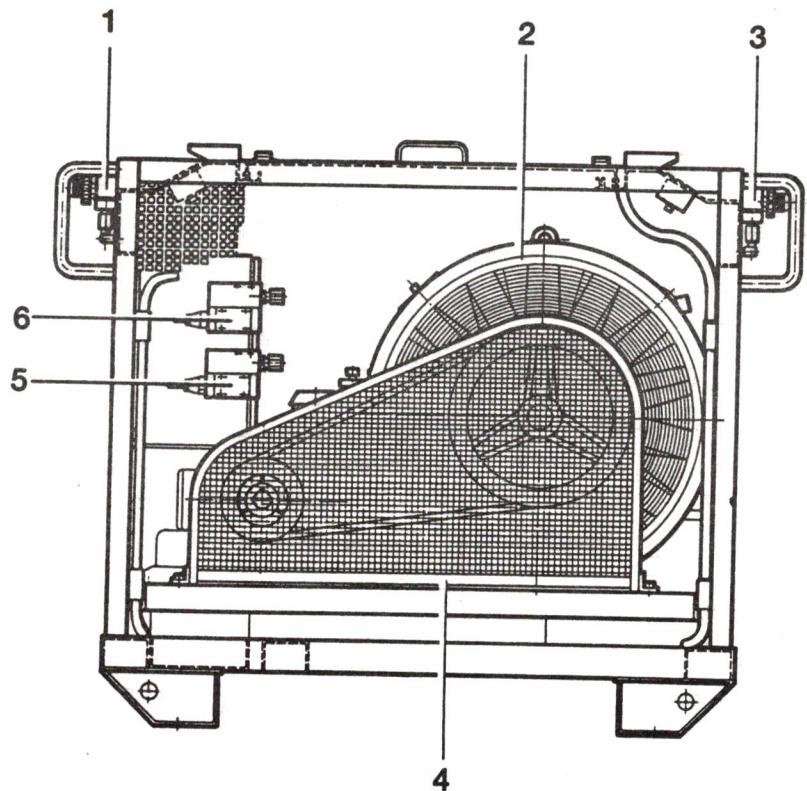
Drucklufterzeuger (EliMot), Rückansicht
